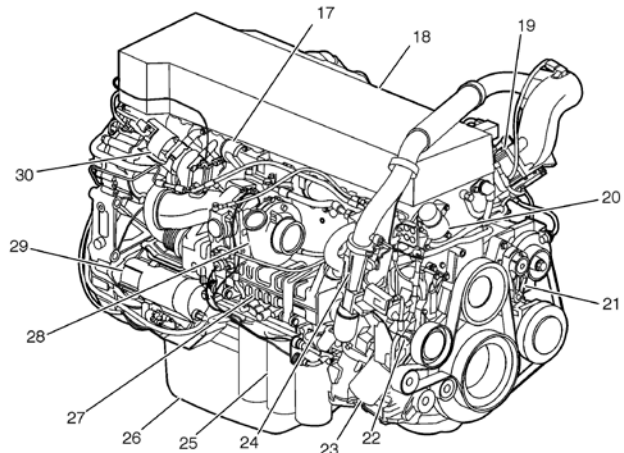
VUE D'ENSEMBLE DU MOTEUR D13H, CÔTÉ TURBOCOMPRESSEUR (TYPIQUE)
